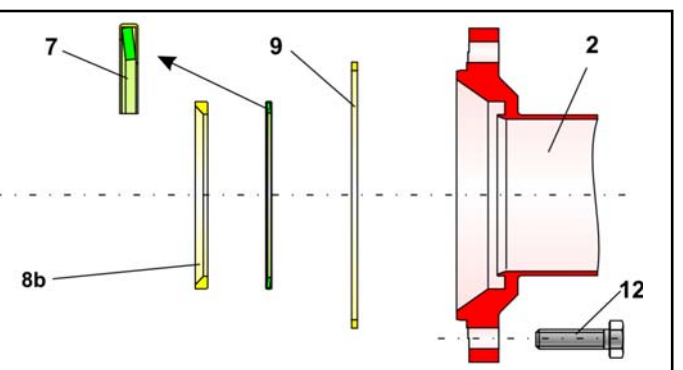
Explosionszeichnung der molchbaren Kugelhähne DN 150
